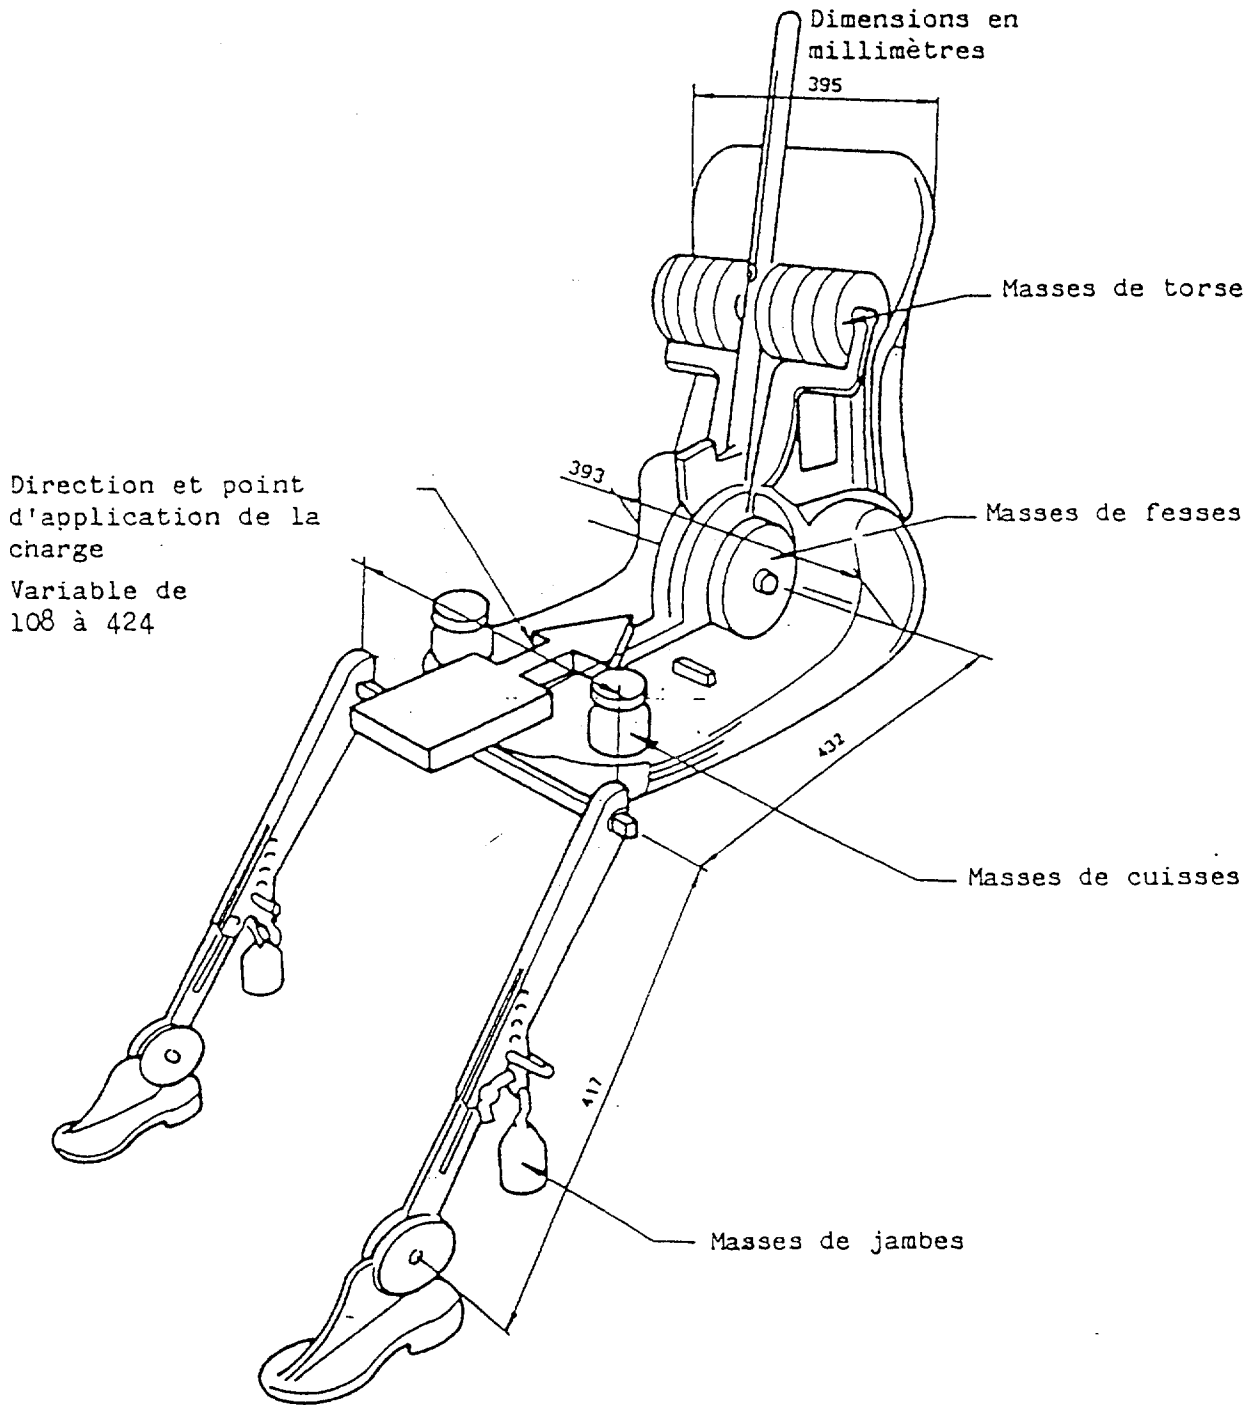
Dimensions des éléments de la machine 3-D H et emplacement des masses
